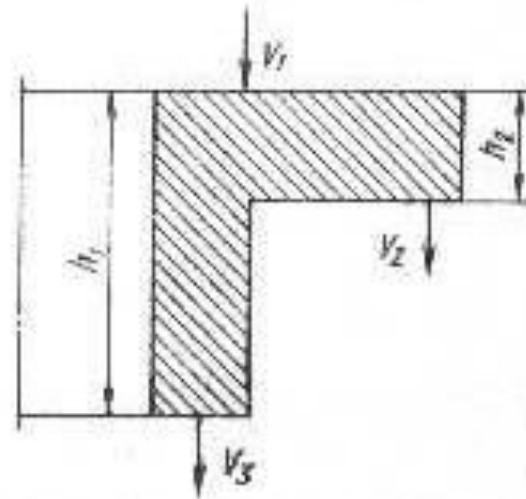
Схема к определению высот лапки и скоростей движения деталей пресс-формы
